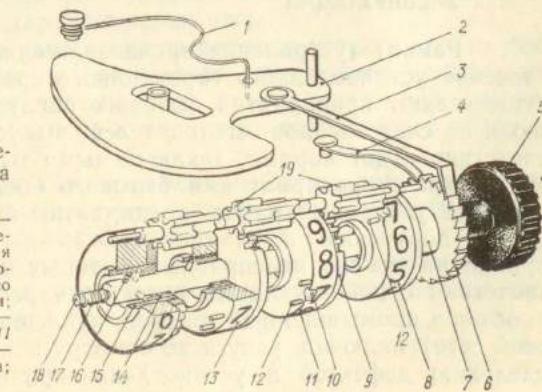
Кинематическая схема шагомера «Заря» ШМ-6:
